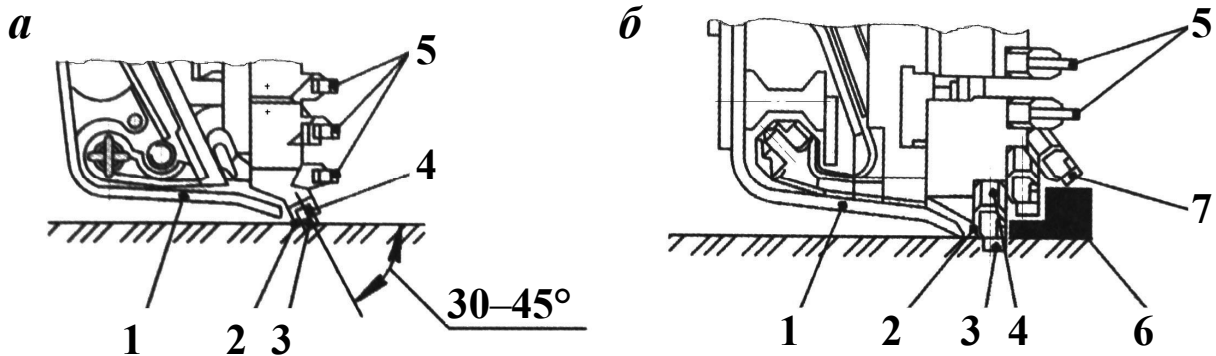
Схемы расположения нижнего (почвенного) резца: *а* – расположение резца под углом к почве; *б* – расположение резца нормально к почве; 1 – угольник направляющей струга; 2 – зона интенсивного износа; 3 – резец почвенный; 4 – резцедержатель; 5 – резцы линейной группы; 6 – угольный уступ; 7 – резец надпочвенный
